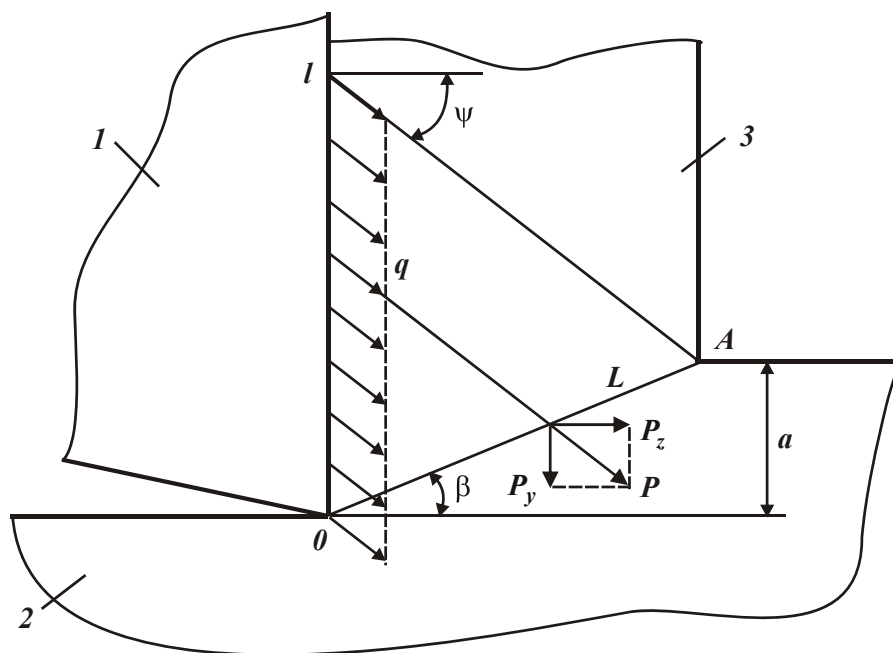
Расчетная схема параметров силовой напряженности процесса резания: 1 – резец; 2 – обрабатываемый материал; 3 – образующая стружка
